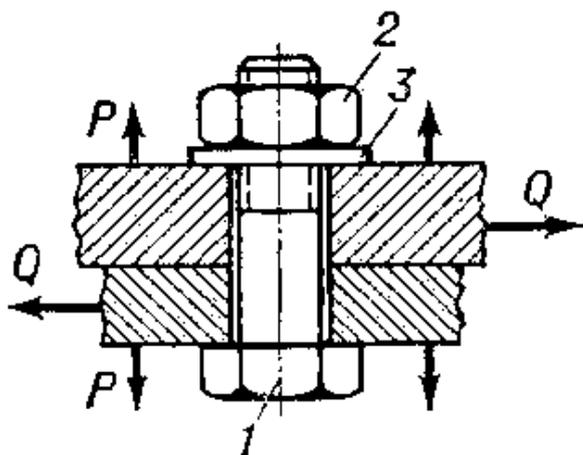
Болтовое соединение с зазором между болтом и отверстием: 1 — болт; 2 — гайка; 3 — шайба.
